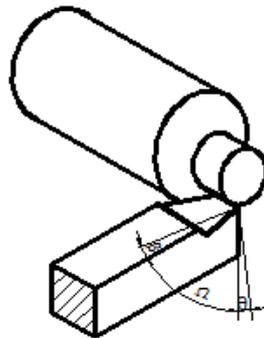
Ángulos que se forman durante la operación del torneado.
